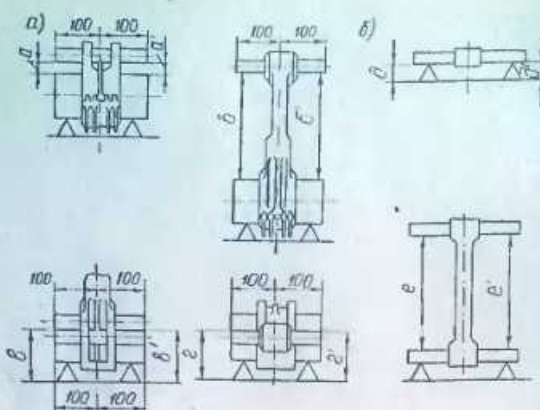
Схема проверки скручивания осей отверстий шатунов:
